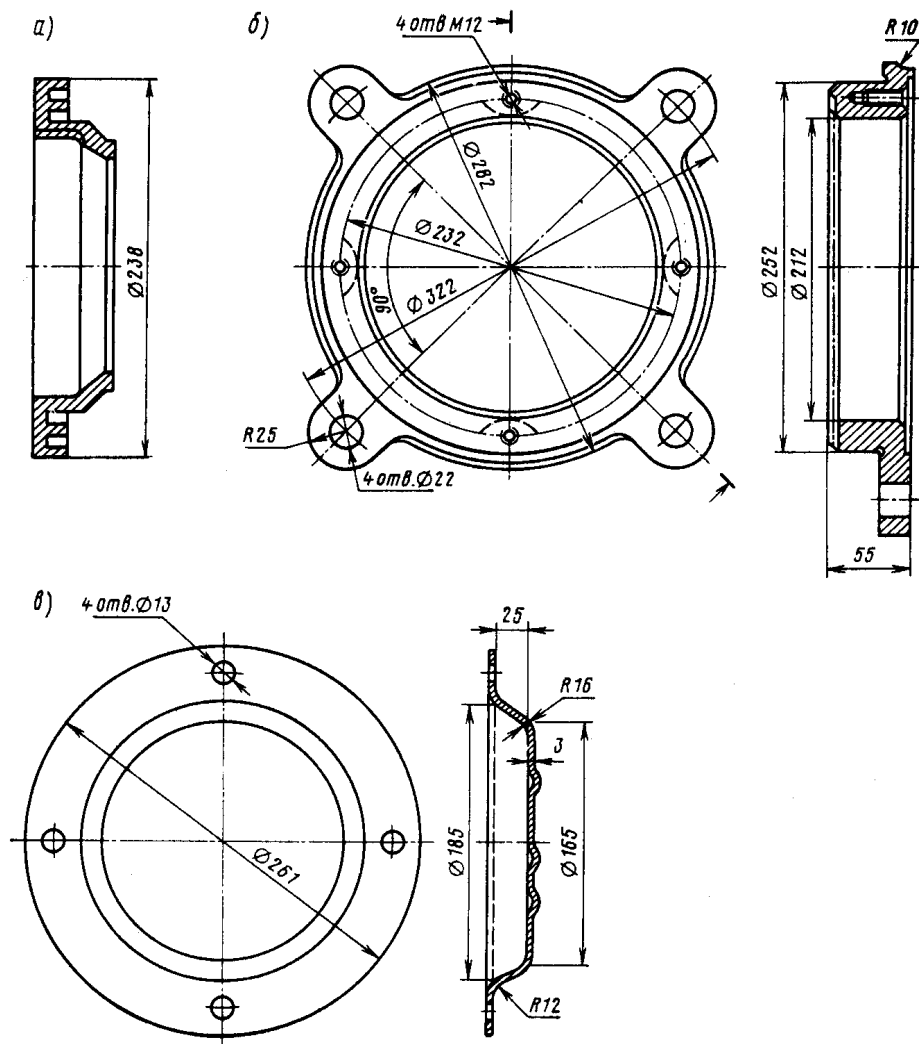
Оглядова і кріпильна кришки буксового вузла
